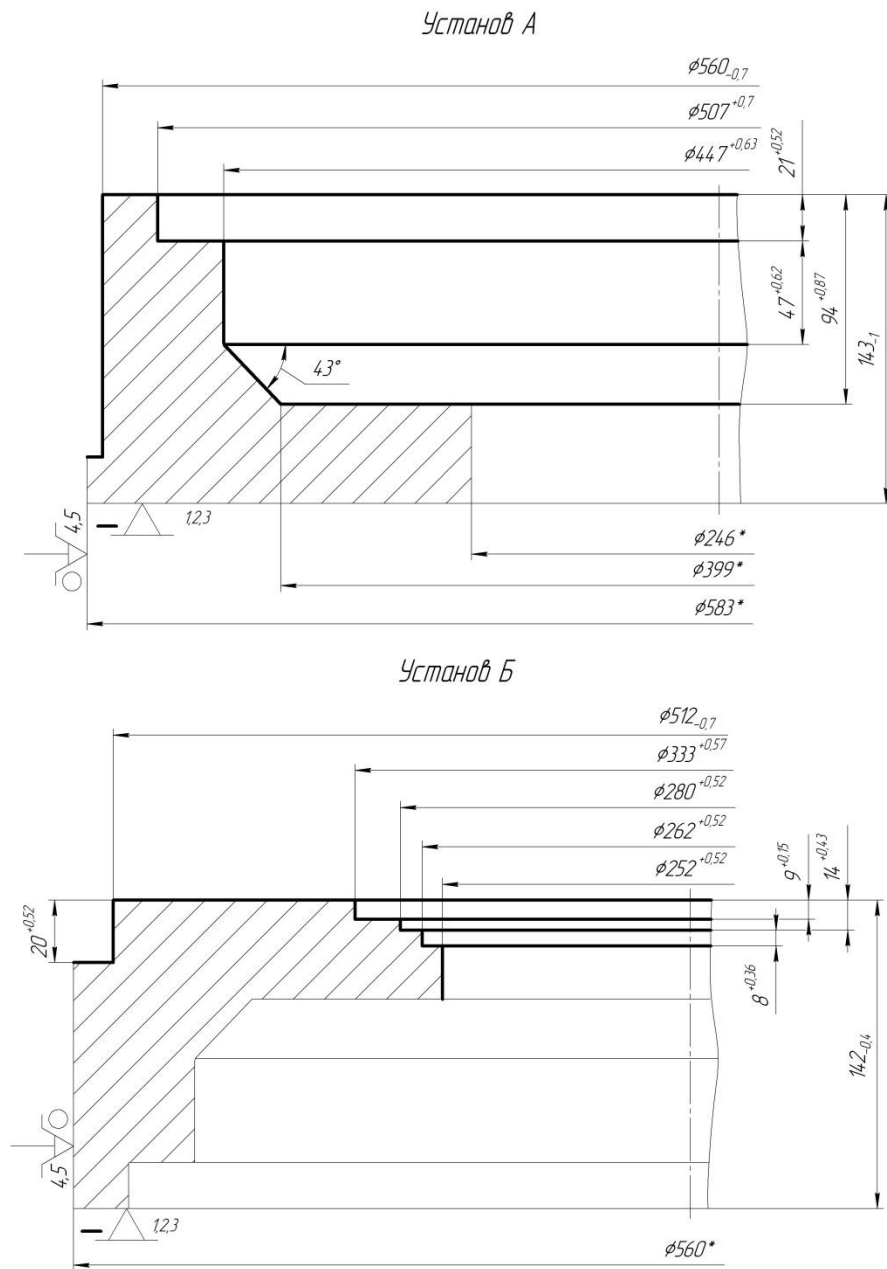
Схема базування заготовки на токарній операції (другий варіант)
